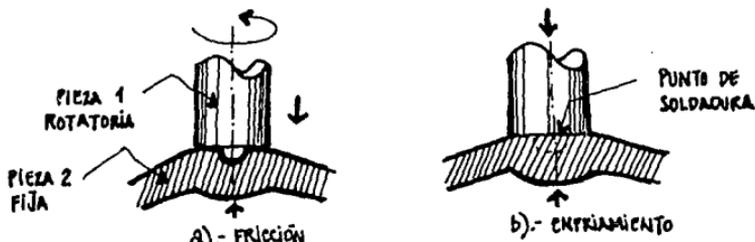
Soldadura por fricción o rotación aplicada como ejemplo a la base de una copa.
